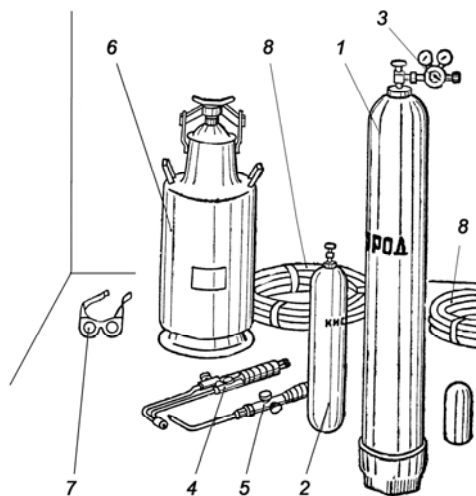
Оборудование для сварки и резки металлов:
